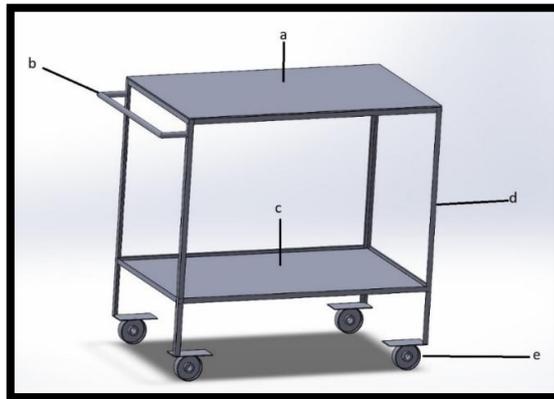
Diseño del banco de soldadura MIG y sus partes.
